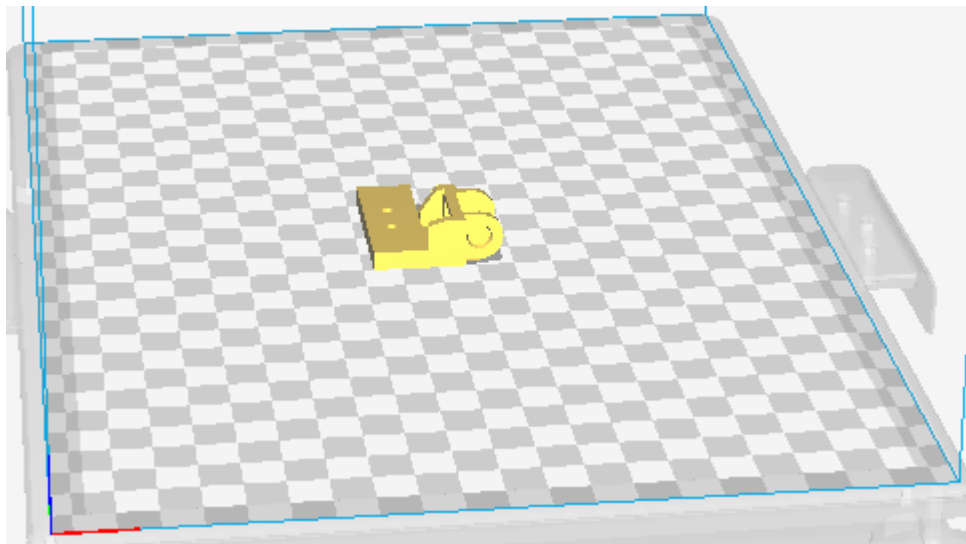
Posición de impresión extremo inicial de cadena portacable 2.
